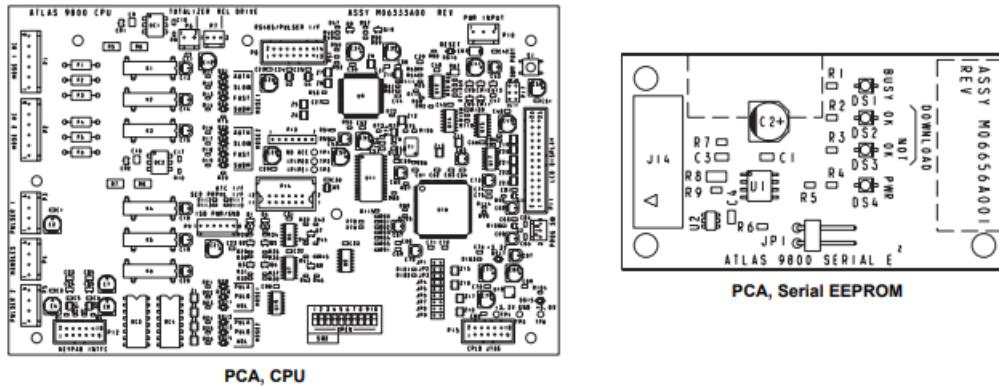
Printed Circuit Assembly de la empresa Gasboy para dispensadores de gasolina
